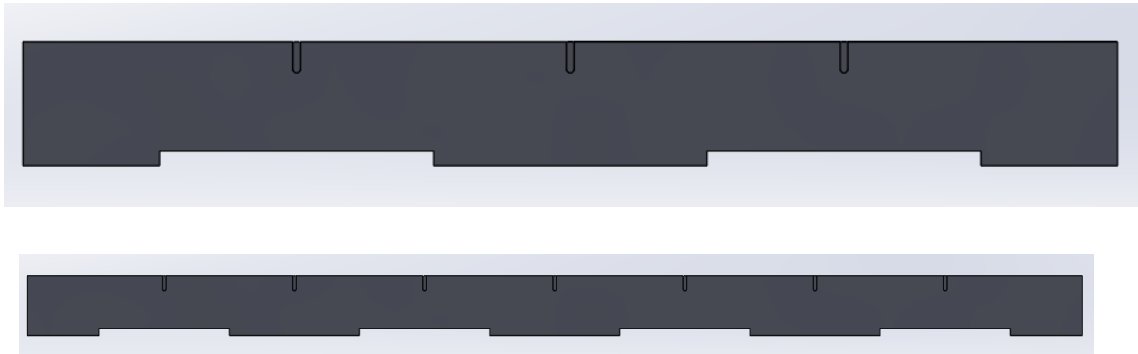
Desenho CAD das placas laterais da mesa de trabalho.
